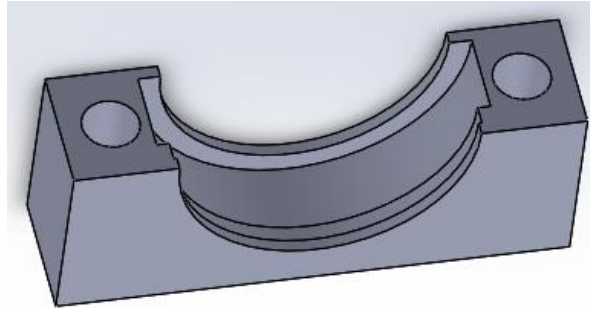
Pieza sujeta rodamiento eje horizontal D25
